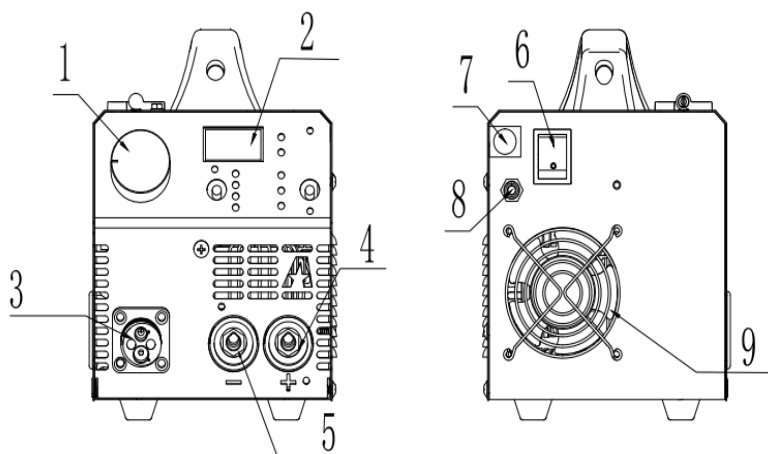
Общий вид (Инверторный сварочный полуавтомат)
